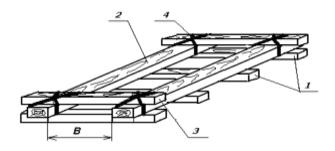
Поддон для рулонов с открытыми торцами 1 – поперечный брусок-подкладка; 2 – продольный опорный брусок; 3 – торцевой упорный брусок; 4 – стяжка
